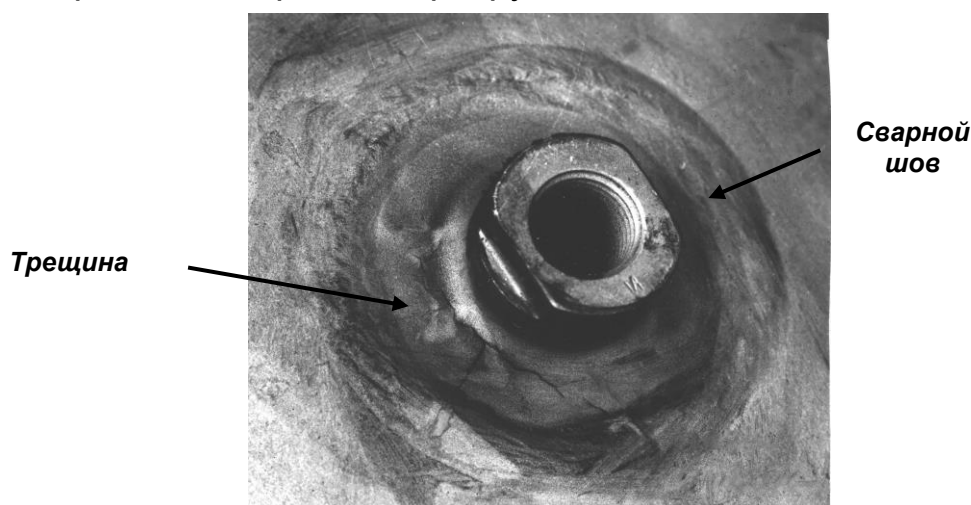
Внешний вид горловины с трещиной в зоне сварного соединения
